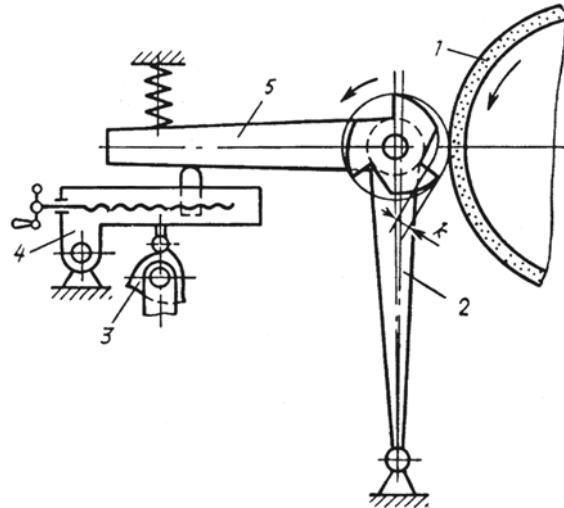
Схема работы станка мод. 4М для радиального затылования метчиков по задней поверхности режущей части:
